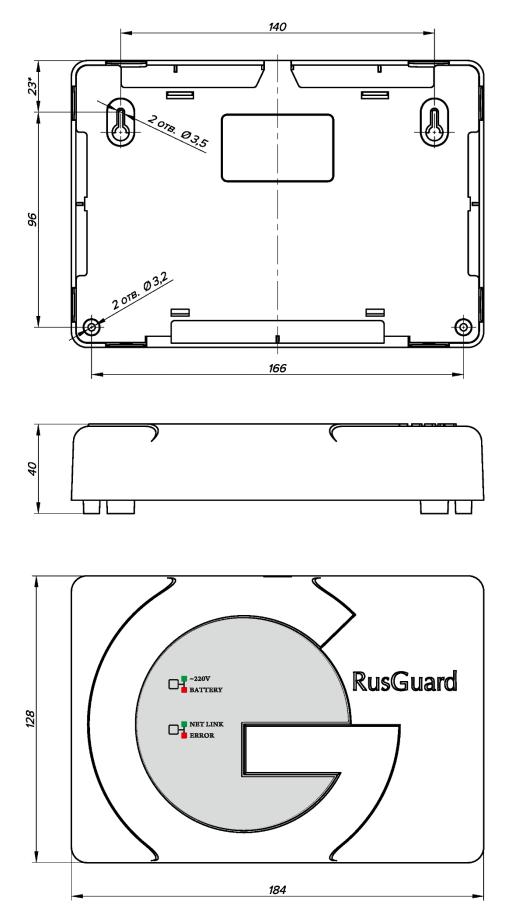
Габаритные размеры и крепеж контроллера в корпусе исполнения -S
